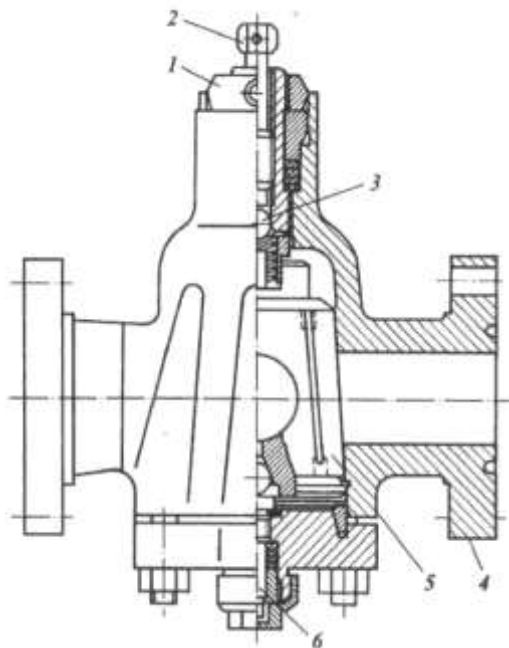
Корковий кран: 1 - рукоятка; 2 - натискний болт; 3 - зворотний клапан; 4 - корпус; 5 - конусна пробка; 6 - гвинт
